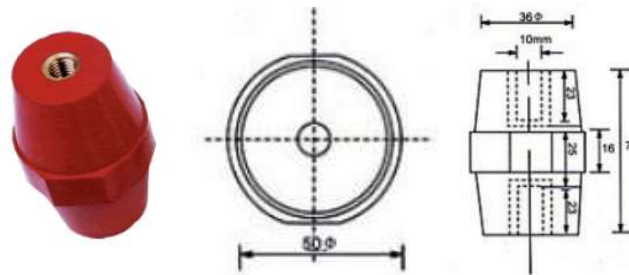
Aislador eléctrico, fabricante EBC, modelo 34076, aislamiento hasta 25 KV.
